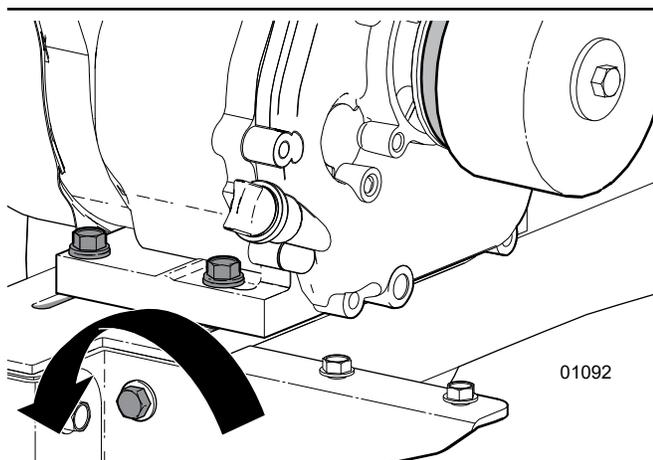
Boulon de réglage de la tension de la courroie d'entraînement
